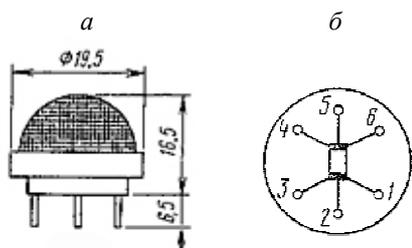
Внешний вид и схематичное изображение датчика газов типа TGS.
